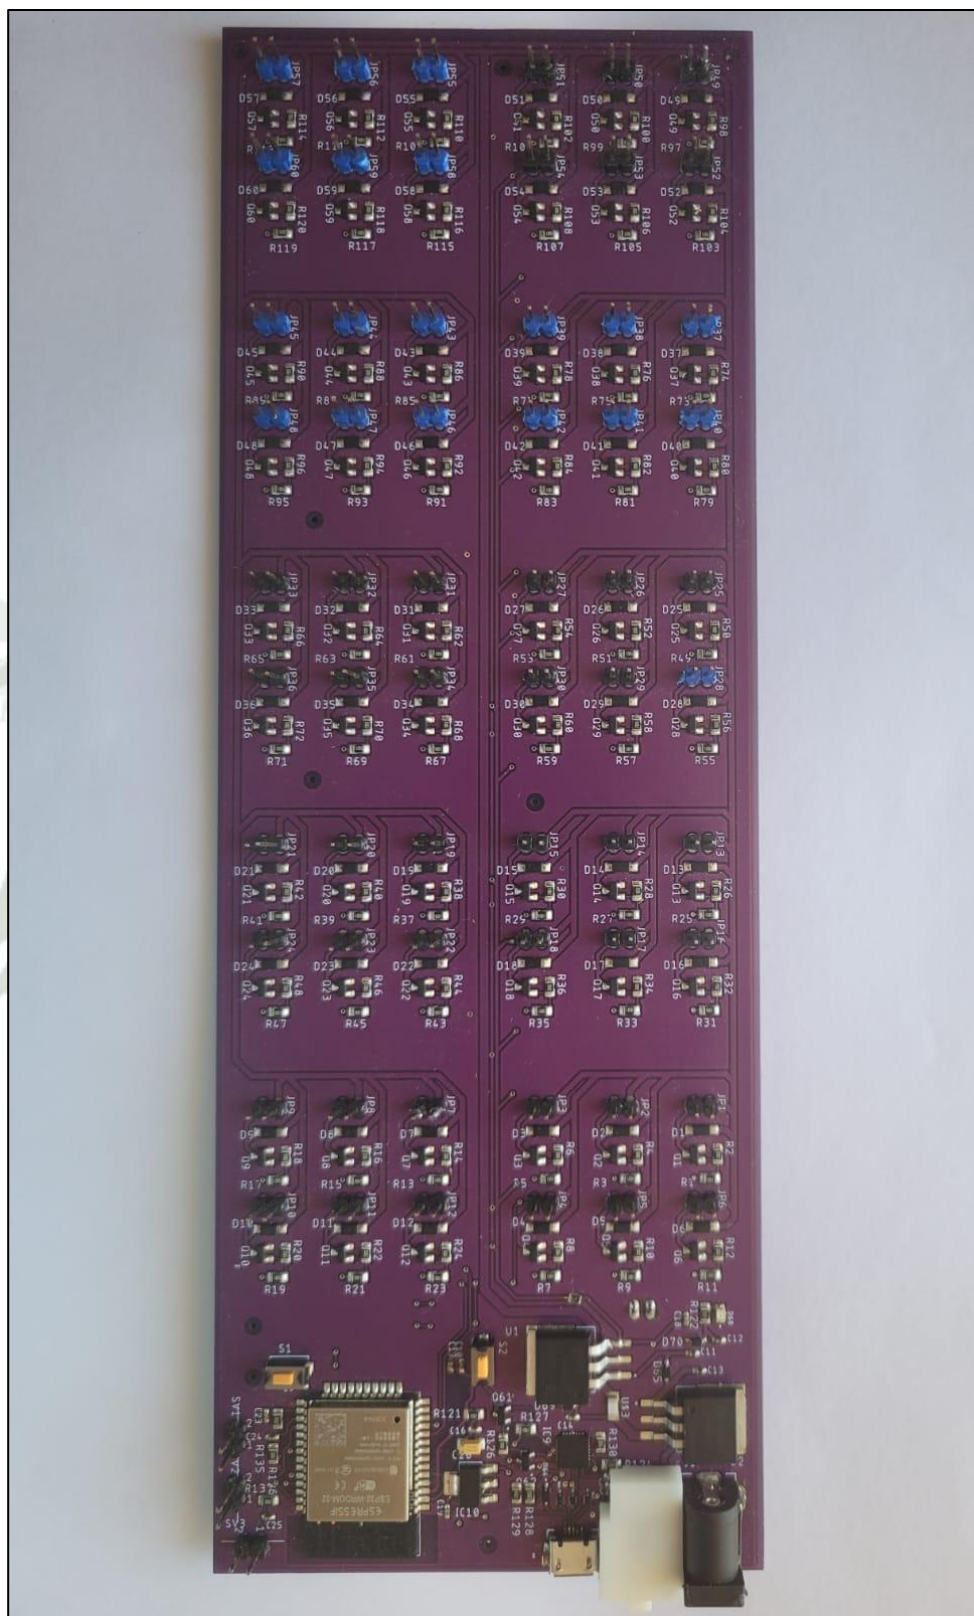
Vista de capa superior PCB con todos los componentes soldados
